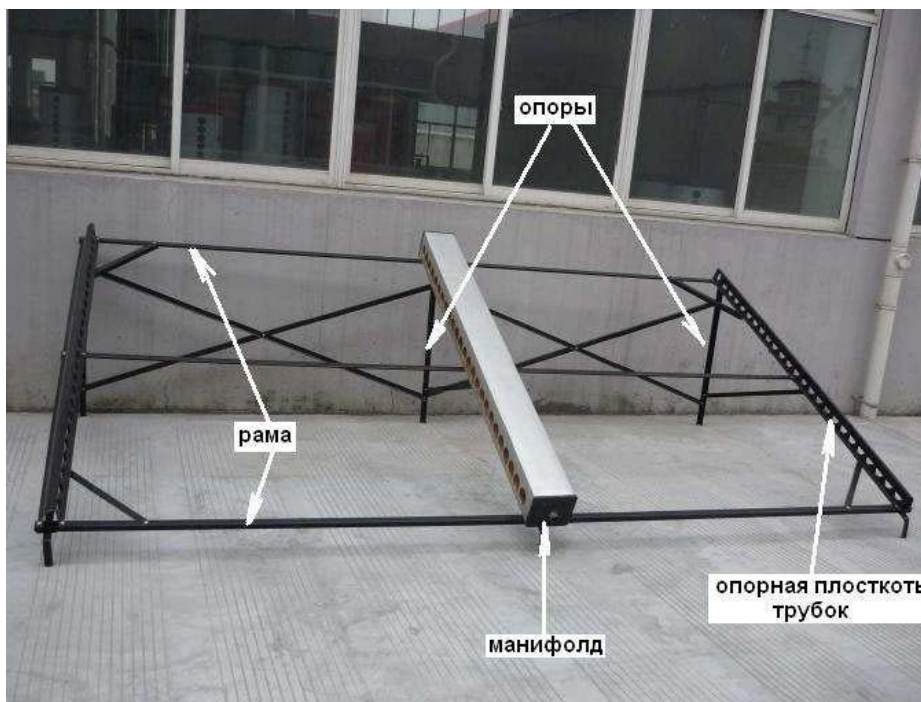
Общий вид в сборе коллектора AC-VG(L)-50 без трубок
